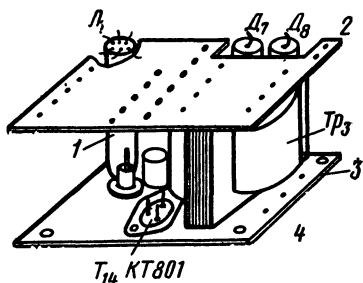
Крепление плат и расположение основных деталей кадрового и выходного строчного каскадов.
